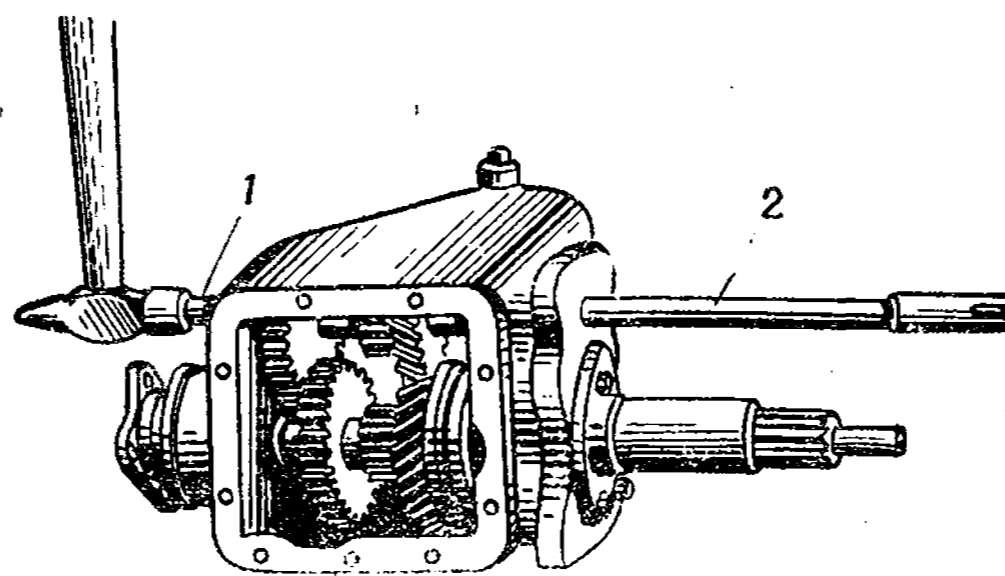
Установка с помощью оправки блока шестерен в картер коробки передач:
